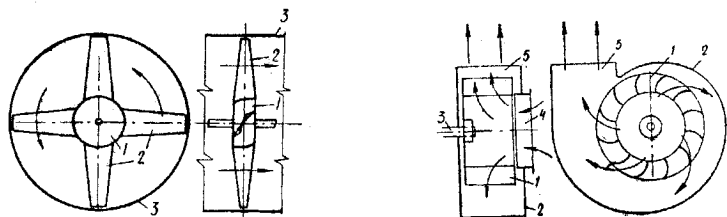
Вентилятори: а – осьовий: 1 – колесо, 2 – лопатки, 3 – корпус; б – відцентровий: 1 – лопаткове колесо, 2 – корпус, 3 – привод, 4 – вхідний отвір, 5 – випускний отвір.
